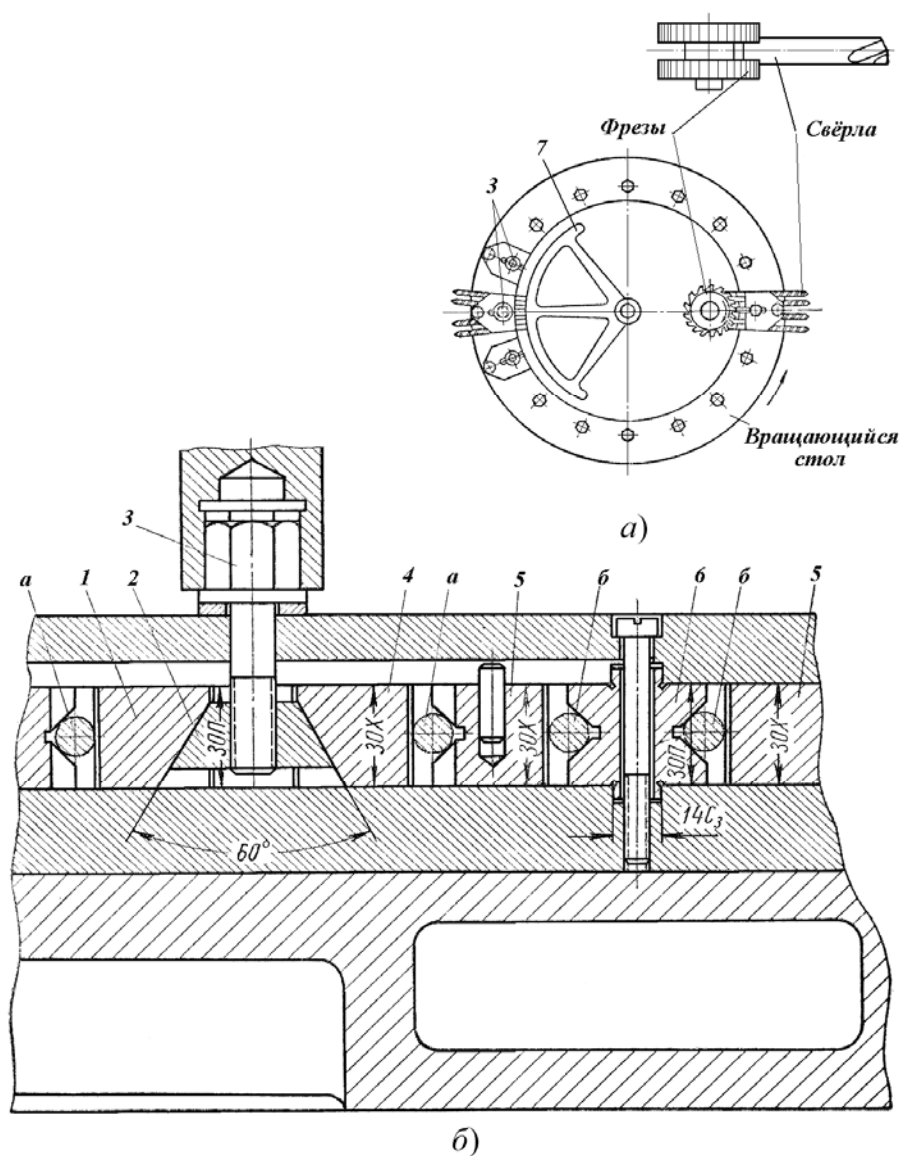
Эскиз приспособления для фрезерования лапок хвостового инструмента
